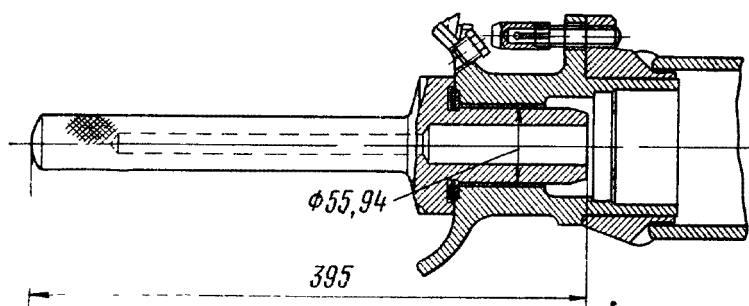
Оправка для запрессовки шаровой опоры в картер переднего моста
